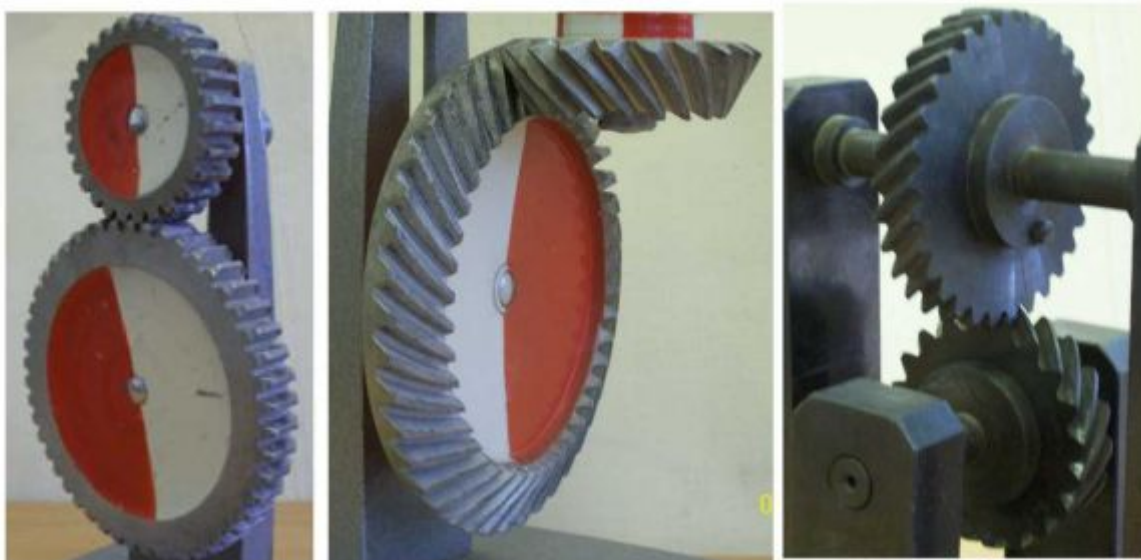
Типы зубчатых передач: цилиндрическая (слева), коническая (в центре), винтовая зубчатая передача
